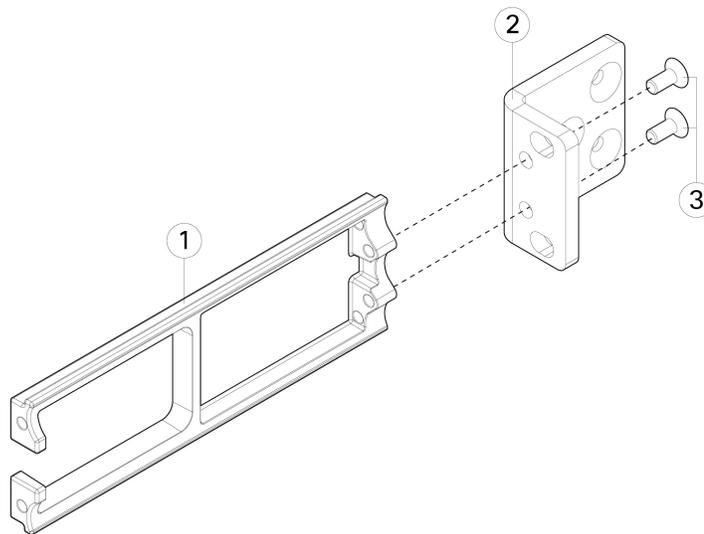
Fixar o suporte de montagem em bastidor no lado do chassi
